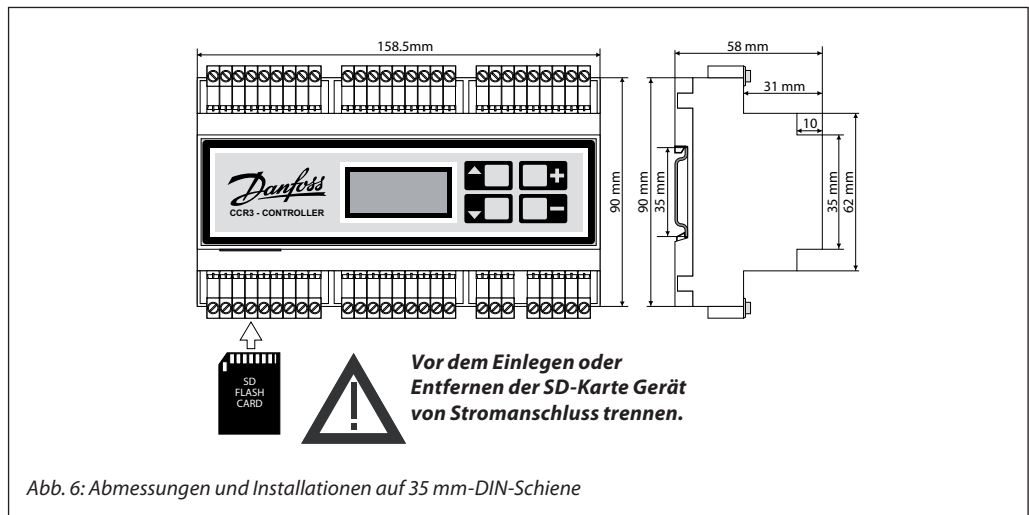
Abmessungen und Installationen auf 35 mm-DIN-Schiene
